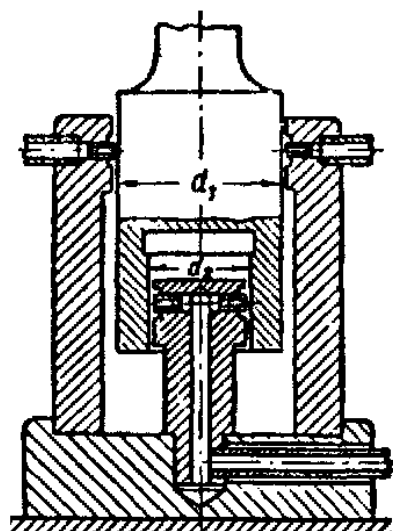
Багатовимірний пристрій для контролю зовнішнього і внутрішнього діаметрів деталі
